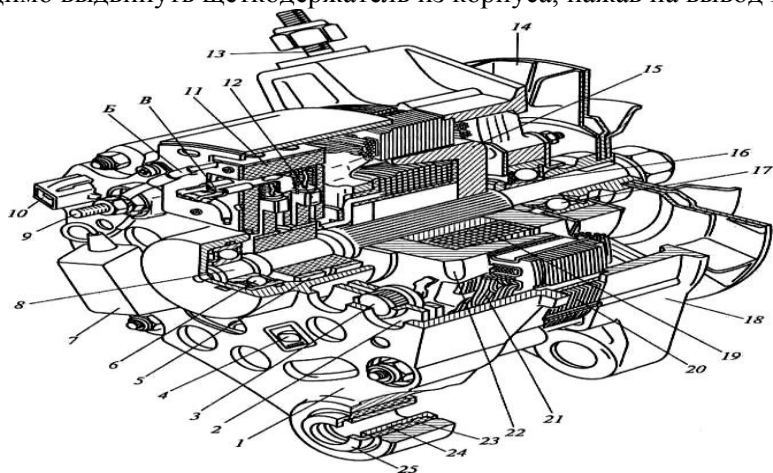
Генератор: 1 — крышка со стороны контактных колец; 2 — выпрямительный блок; 3 — вентиль выпрямительного блока; 4 — винт крепления выпрямительного блока; 5 — контактное кольцо; 6 — задний шарикоподшипник; 7 — конденсатор; 8 — вал ротора; 9 — вывод клеммы «30» генератора; 10 — вывод штекера «61» генератора; 11 — регулятор напряжения; 12 — щетка; 13 — шпилька крепления генератора к натяжной планке; 14 — шкив с вентилятором; 15 — полюсный наконечник ротора; 16 — дистанционная втулка; 17 — передний шарикоподшипник; 18 — крышка привода; 19 — обмотка ротора; 20 — статор; 21 — обмотка статора; 22 — полюсный наконечник ротора; 23 — буферная втулка; 24 — втулка; 25 — поджимная втулка; Б, В — выходы регулятора напряжения
